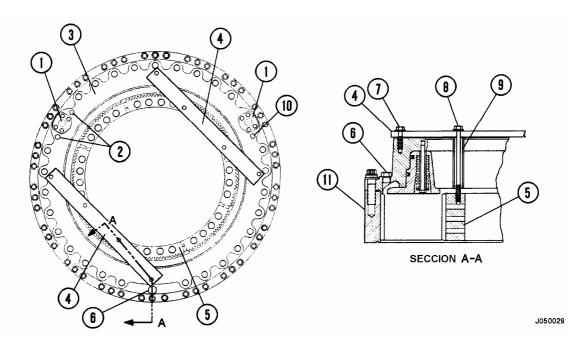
MONTAJE DEL ENGRANAJE INTERNO
